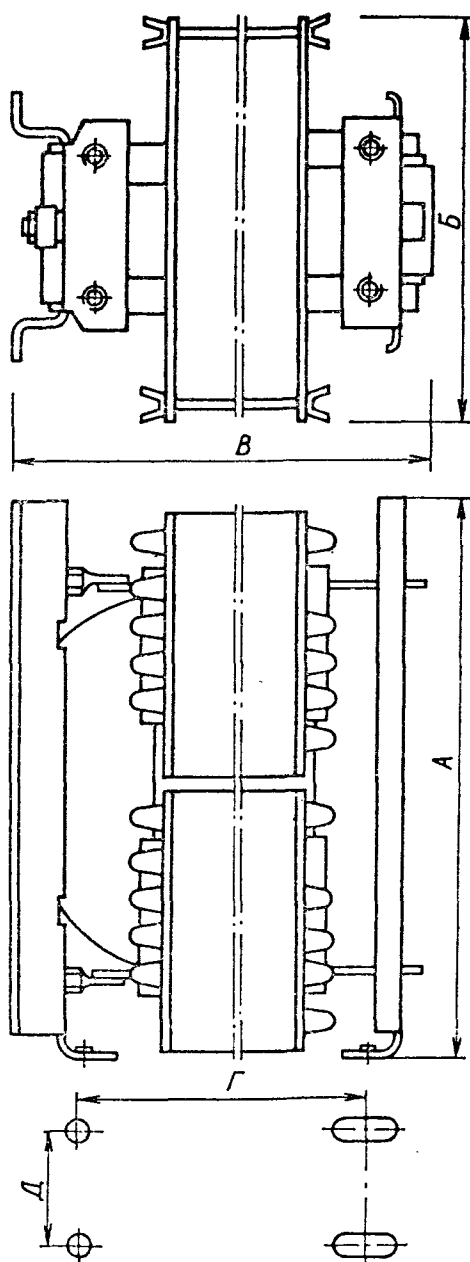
Габаритный чертеж и размеры для крепления силовых трансформаторов
